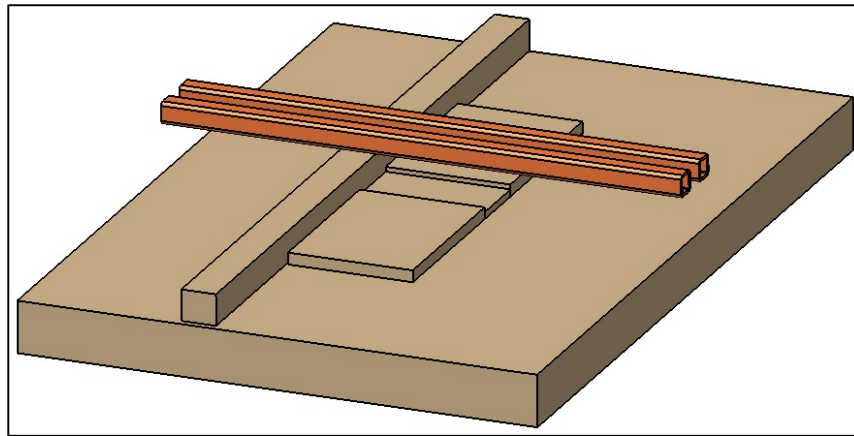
Positionnement du support pour deuxième soudure
